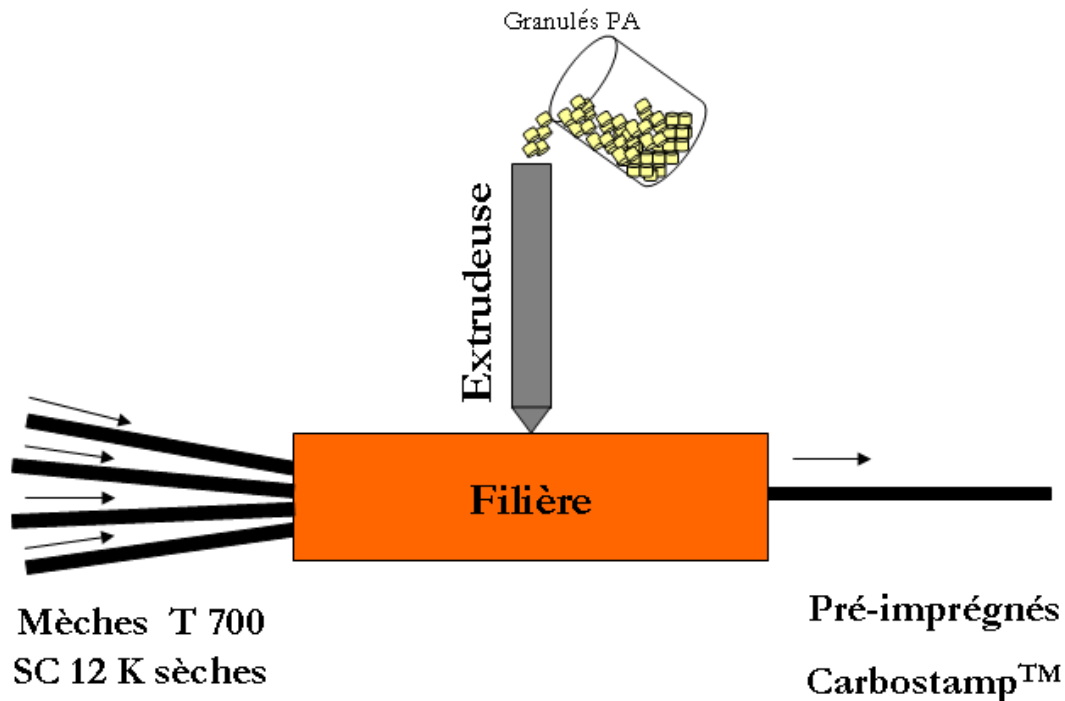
Technique d'imprégnation des fibres de carbone dédiée à la fabrication des pré-imprégnés Carbostamp®
